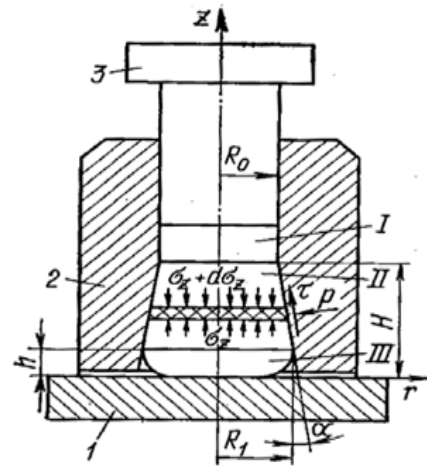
Схема получения заготовки в подвижной обойме: 1 – плита; 2 – обойма; 3 – пуансон
